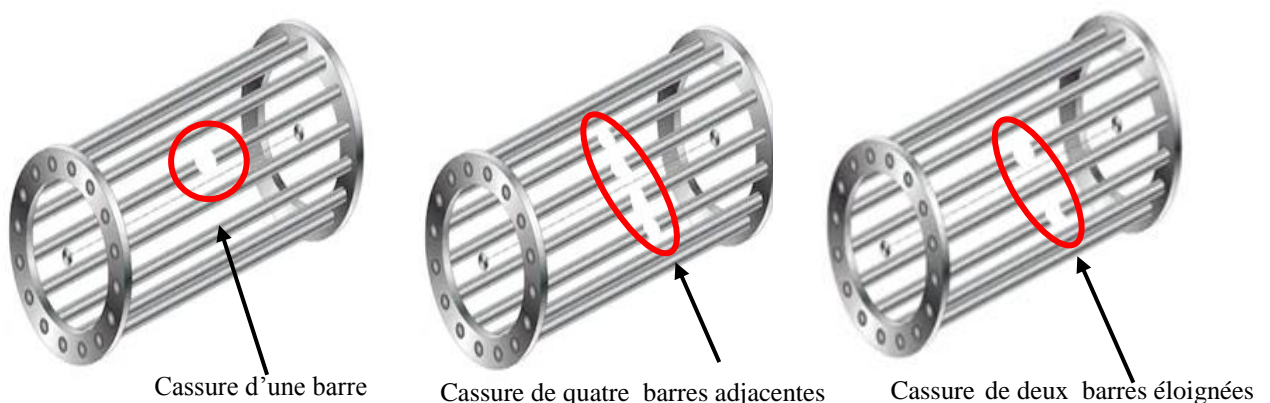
Cassure des barres de rotor à cage d'écureuil [6]
